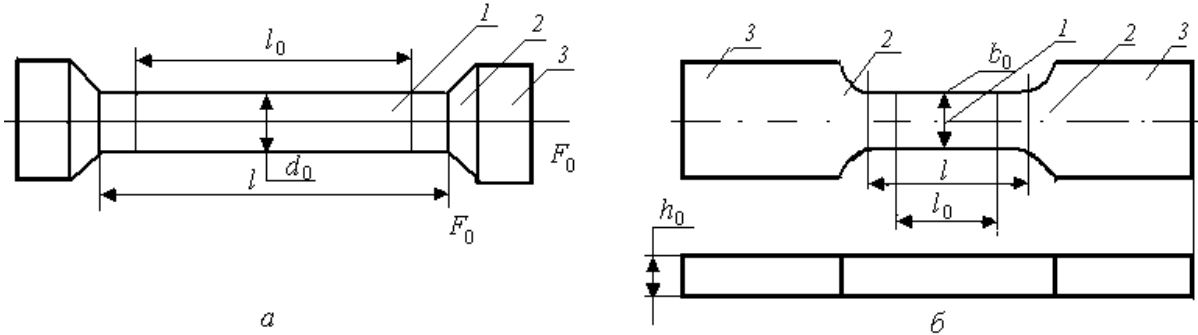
Циліндричний (а) та плоский (б) зразки: 1 – робоча ділянка, 2 – перехідна ділянка, 3 – головка зразка; l - довжина робочої ділянки, l_0 - початкова розрахункова довжина, яка відповідає базі вимірювань, (тобто відстані між опорами тензметра, що вимірює деформації), h_0 і b_0 – початкова товщина та ширина робочої ділянки листового зразка
